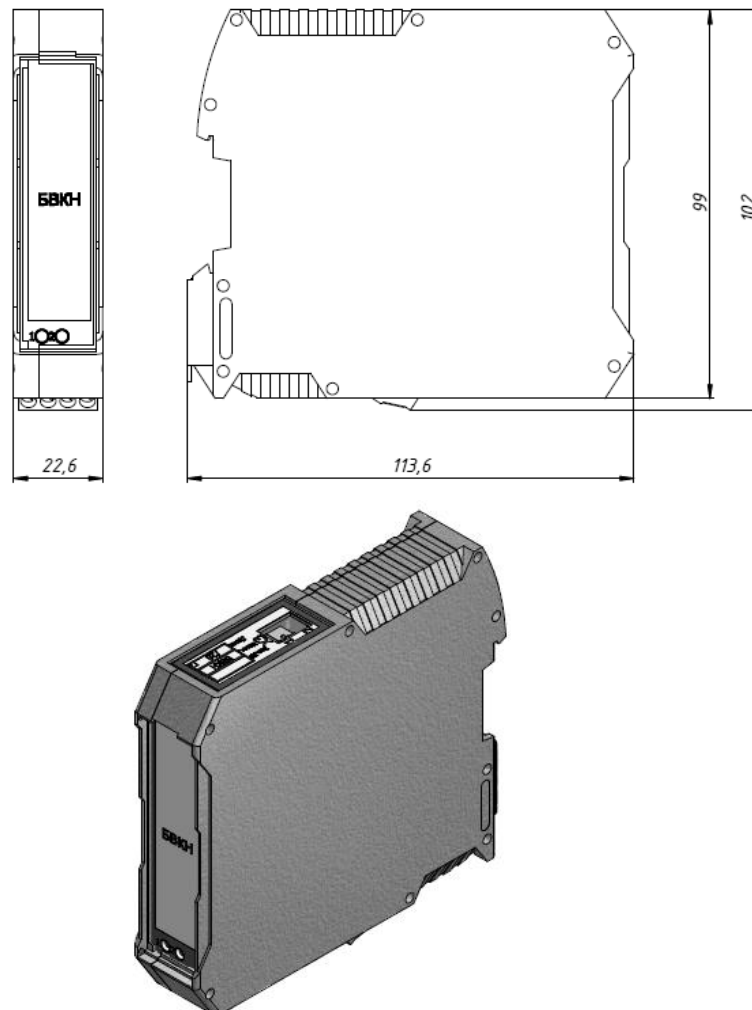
Внешний вид и габаритные размеры БВКН-1
